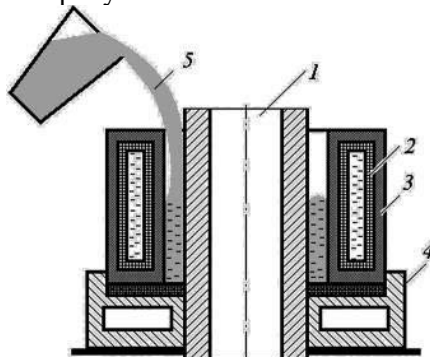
Схема індукційного наплавлення заливанням рідкого присадного металу на підігрітий основний метал: 1 – оброблювана деталь; 2 – індуктор; 3 – вогнетривкий склад; 4 – водоохолоджуване кільце; 5 – метал.
